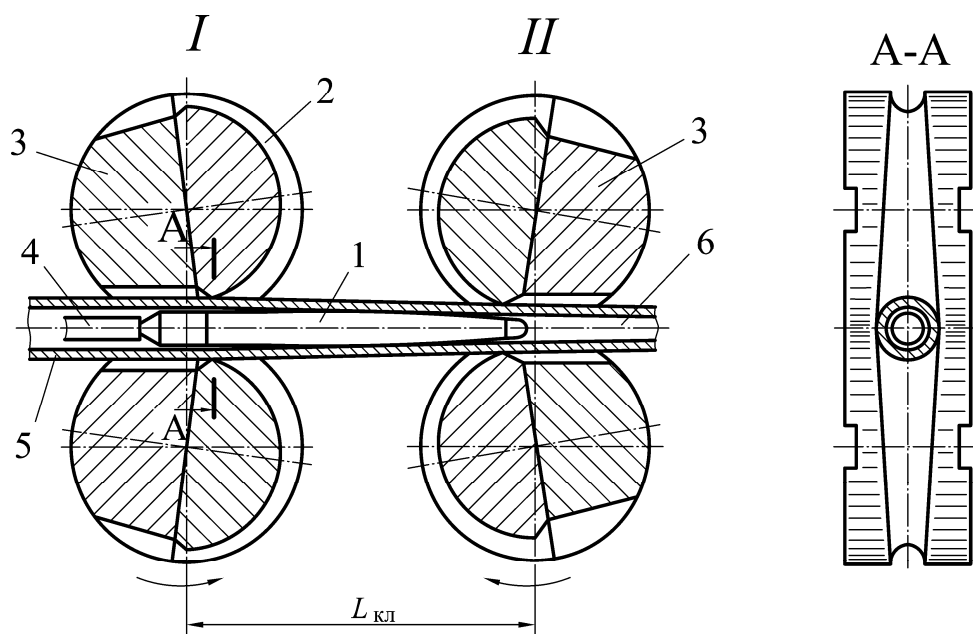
Схема прокатки труб на стане ХПТ: 1 – оправка; 2 – калибр; 3 – валок; 4 – стержень; 5 – заготовка; 6 – труба
